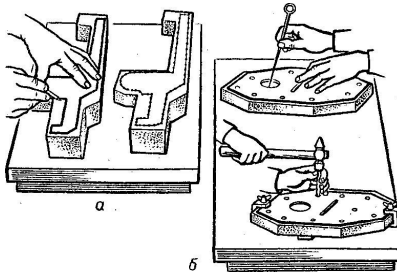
Розмічання за шаблоном: а – робота рисувалкою та розмічена заготовка ; б – робота рисувалкою та накернювання центрів для отворів
